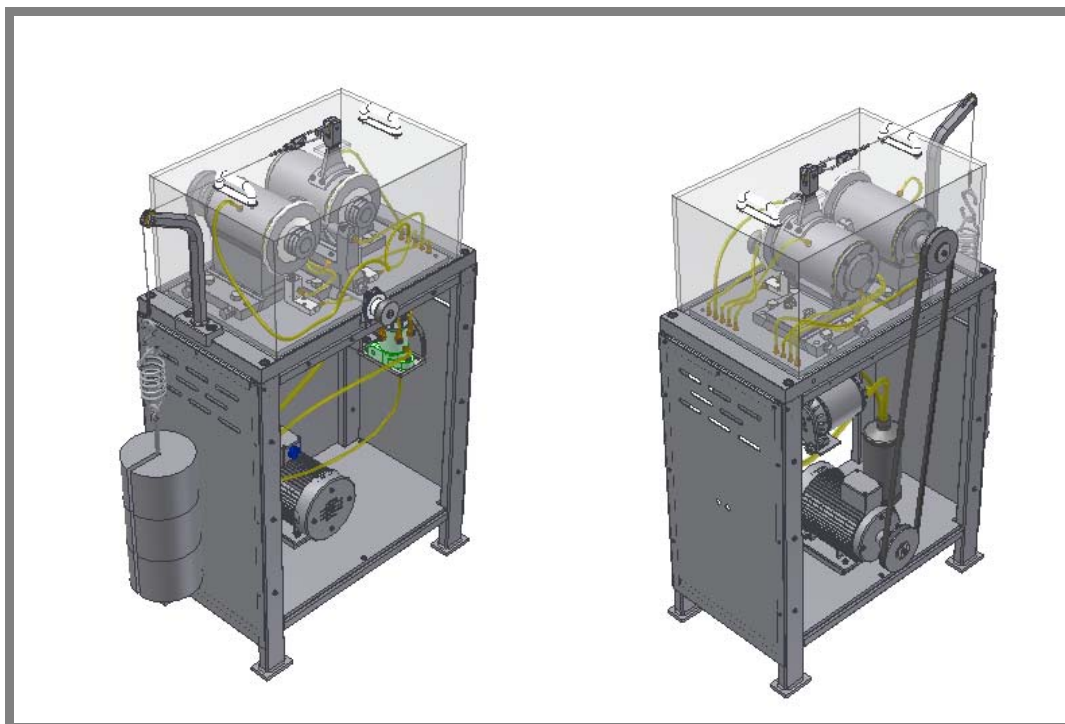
Zkušební zařízení UTM 2 000 Twin disc [43]
